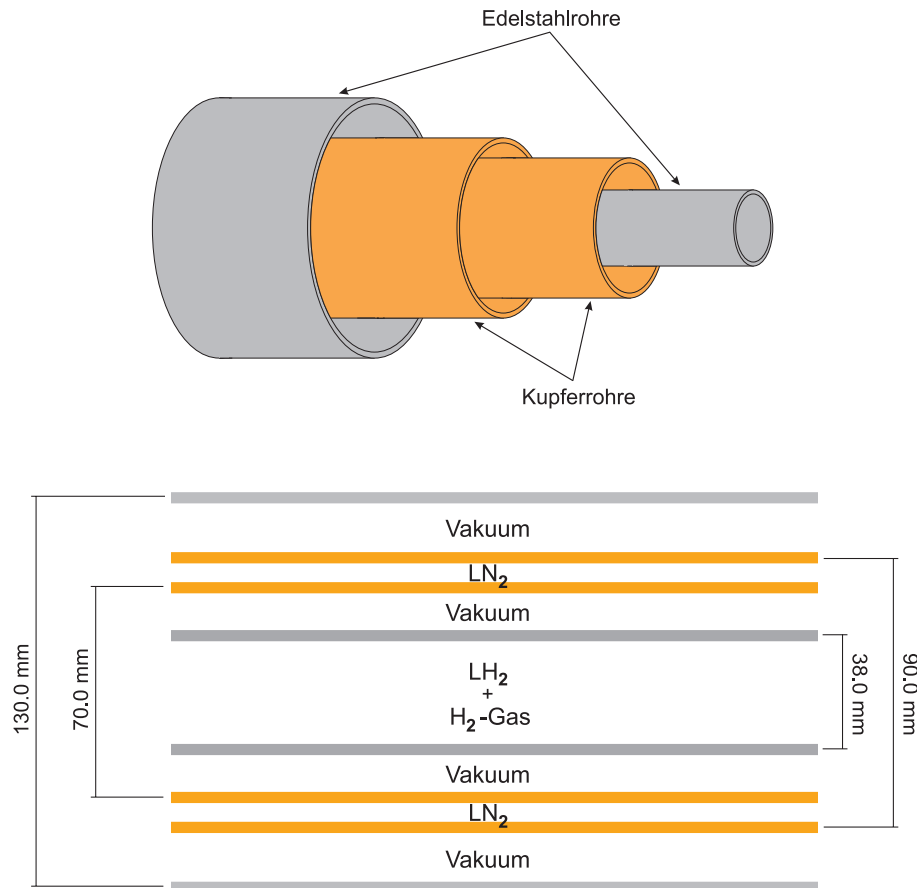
Schnitte durch die stickstoffgekühlte Transferleitung. Das obere Bild zeigt einen Quer-, das untere Bild einen Längsschnitt.
